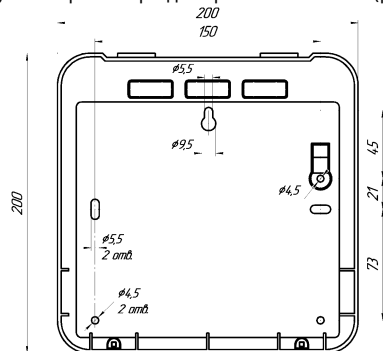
Розмітка отворів для кріплення корпусу модуля
